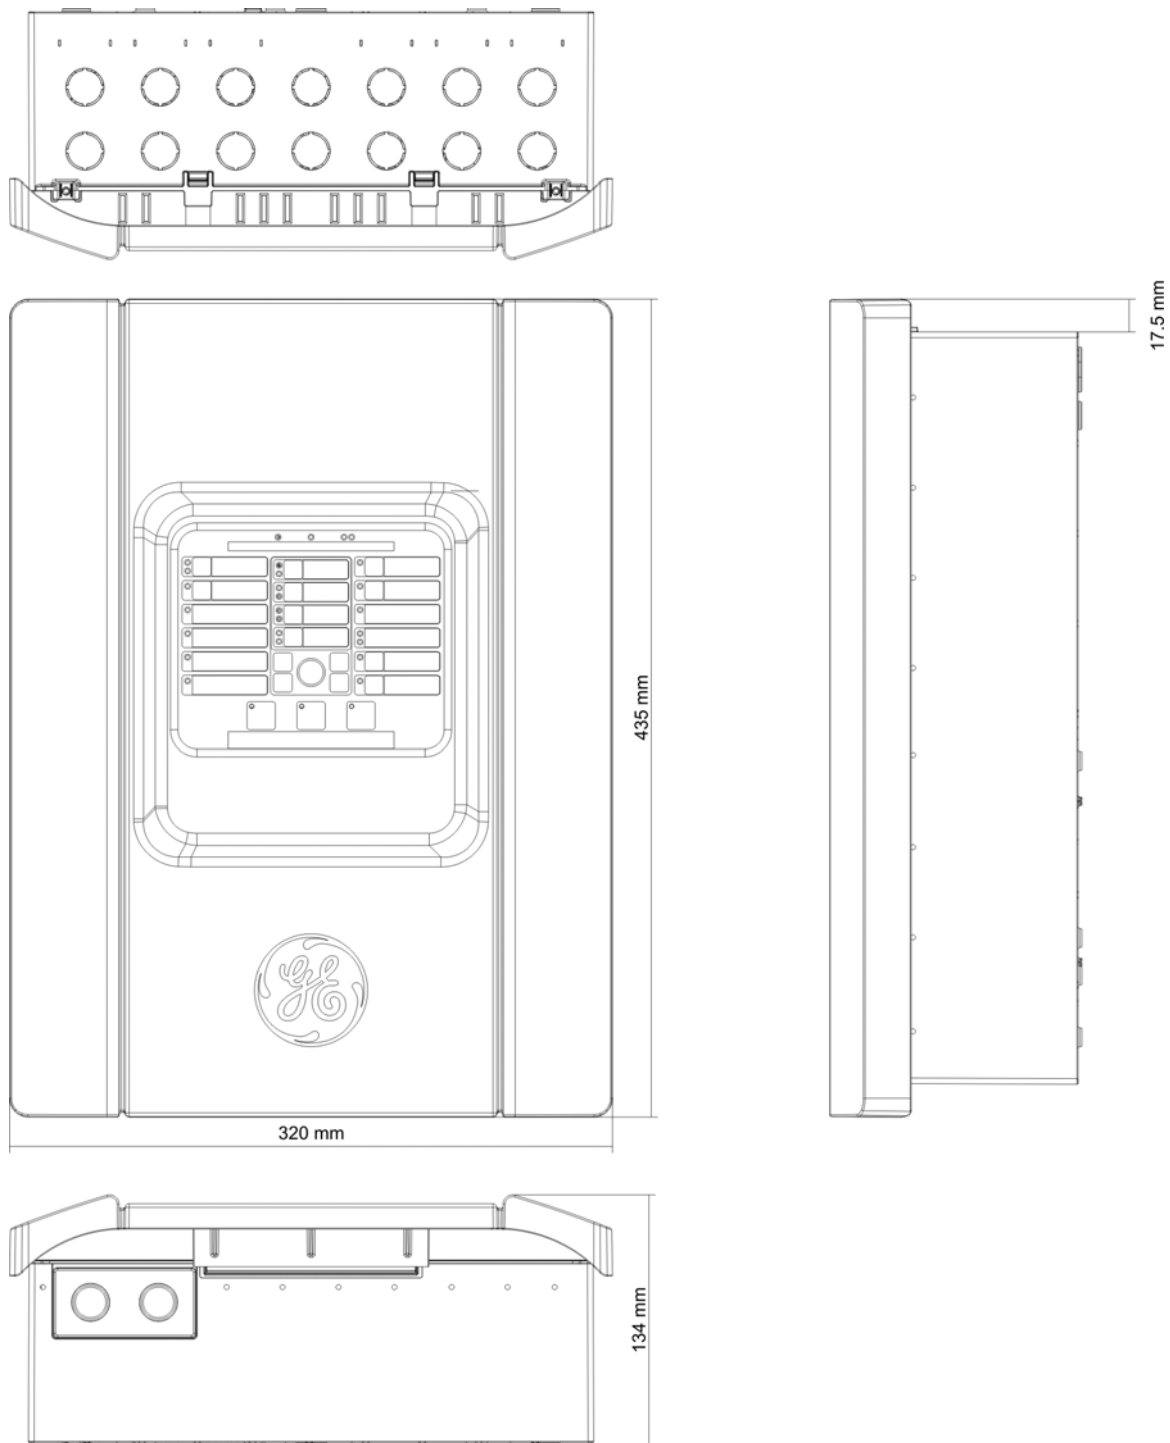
Двухзонный и четырехзонный шкаф без крышки
